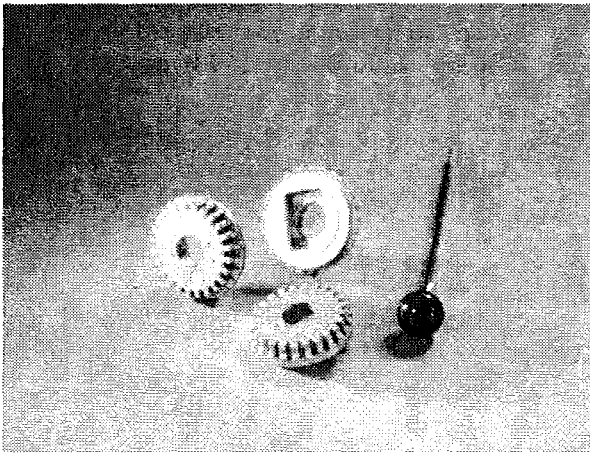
Rastrad für feinwerktechnisches Gerät (Schunk Sintermetalltechnik GmbH, Gießen).
